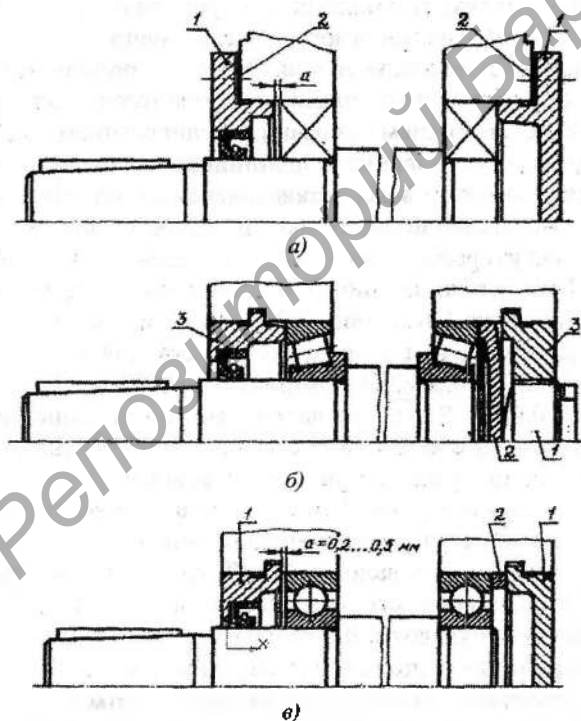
Схема установки подшипников «враспор» [9, с. 105]
